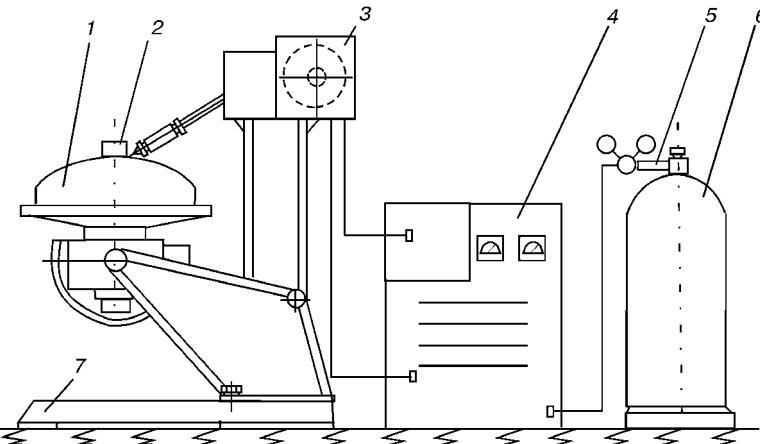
Схема автоматизированной установки для приварки штуцера к днищу в защитном газе: 1 — днище; 2 — штуцер; 3 — механизм подачи проволоки; 4 — источник питания; 5 — газопровод; 6 — баллон с газом; 7 — манипулятор
